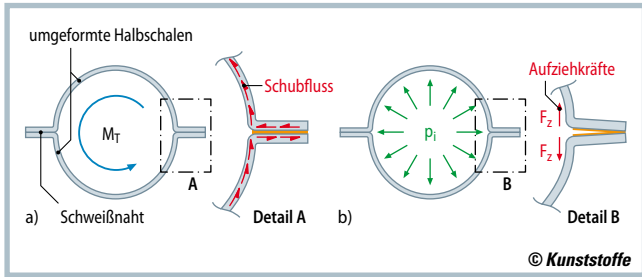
Schweißnaht als Schwachstelle von Hohlprofilen aus flächigen Halbzeugen: a) bei Torsionsbelastung überträgt die unverstärkte Matrix die Kraft durch Schub; b) bei Innendruckbelastung oder einer Ovalisierung des Querschnitts entstehen Aufziehkräfte, die das Versagen in der Schweißnaht begünstigen (Quelle: TU Darmstadt)
